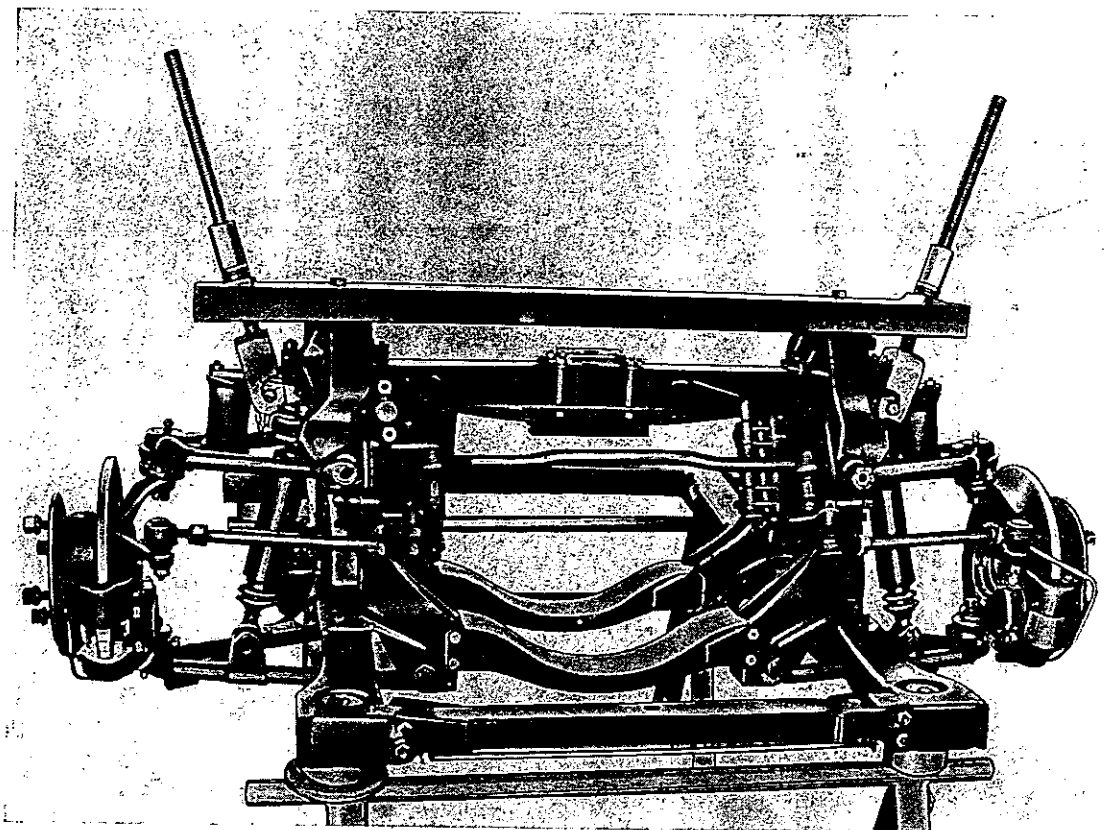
/9 - Châssis auxiliaire sur chevalets.
